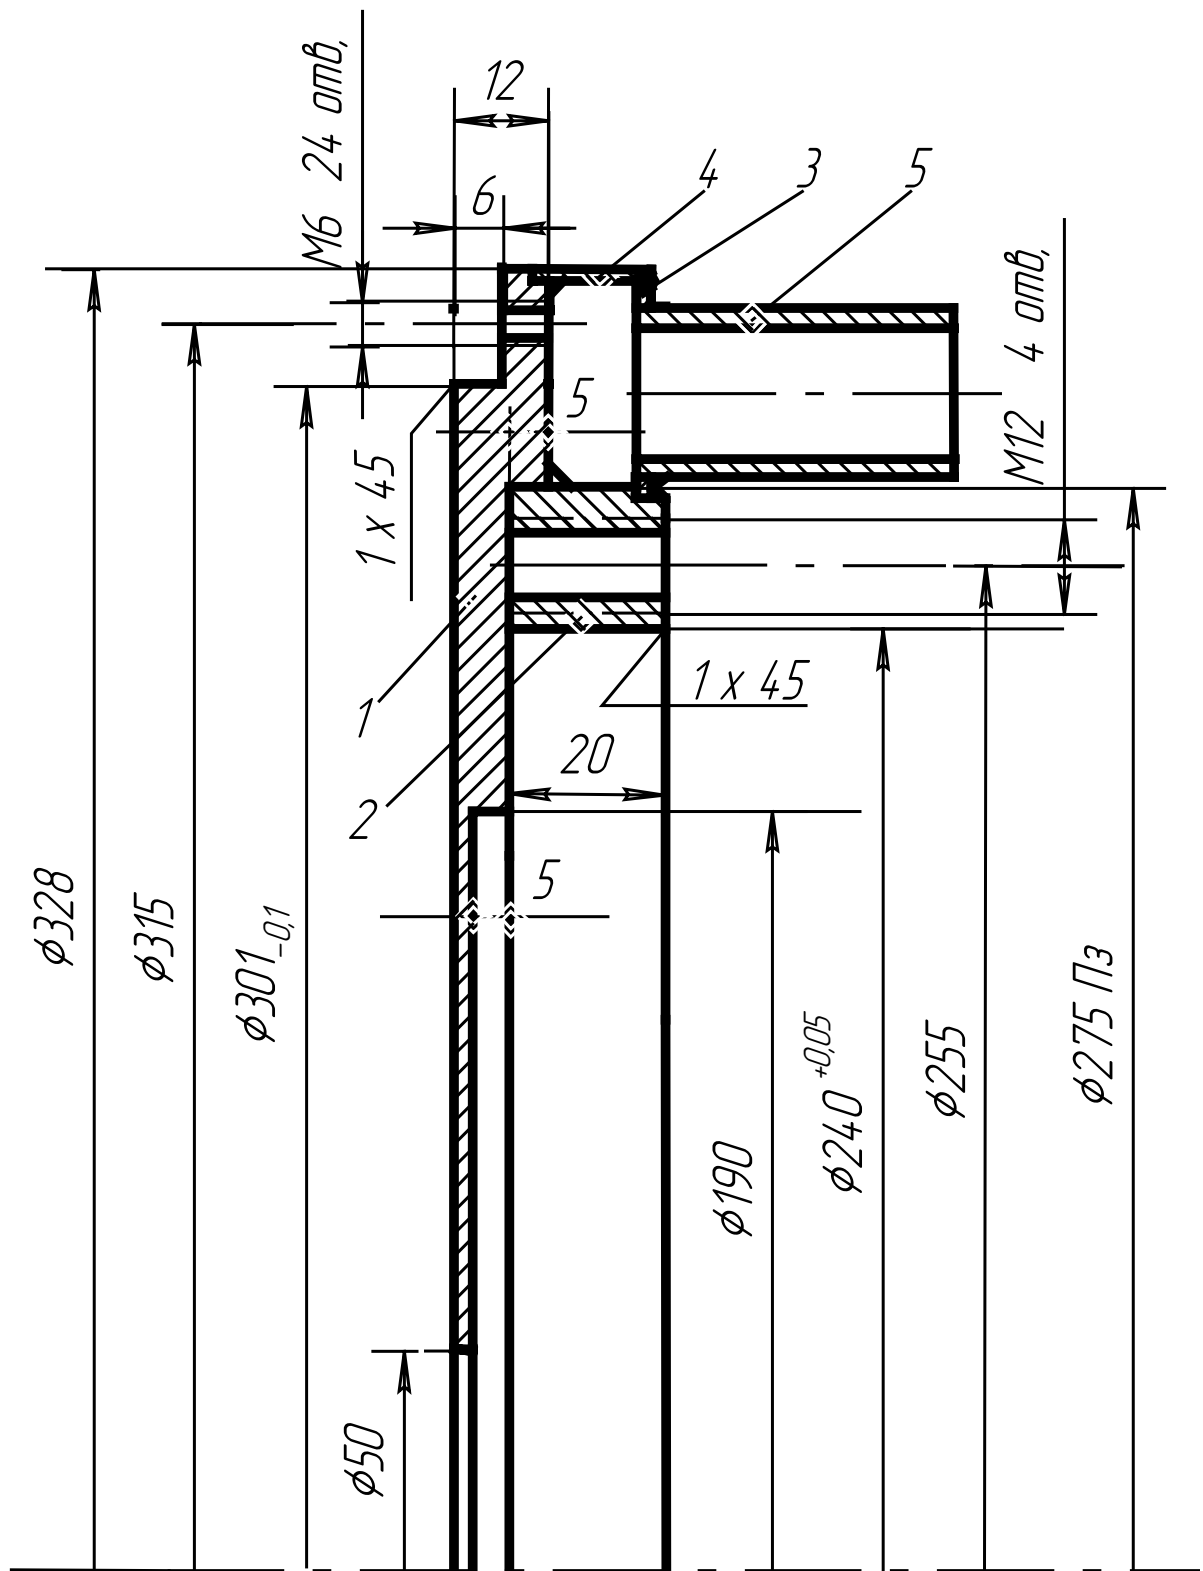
Сварной корпус теплогенератора.
